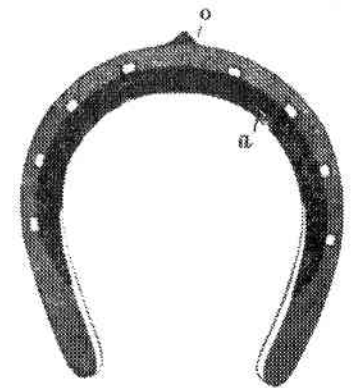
Верхняя поверхность той же подковы: а) бухтовка, б) отворотъ или головка.
